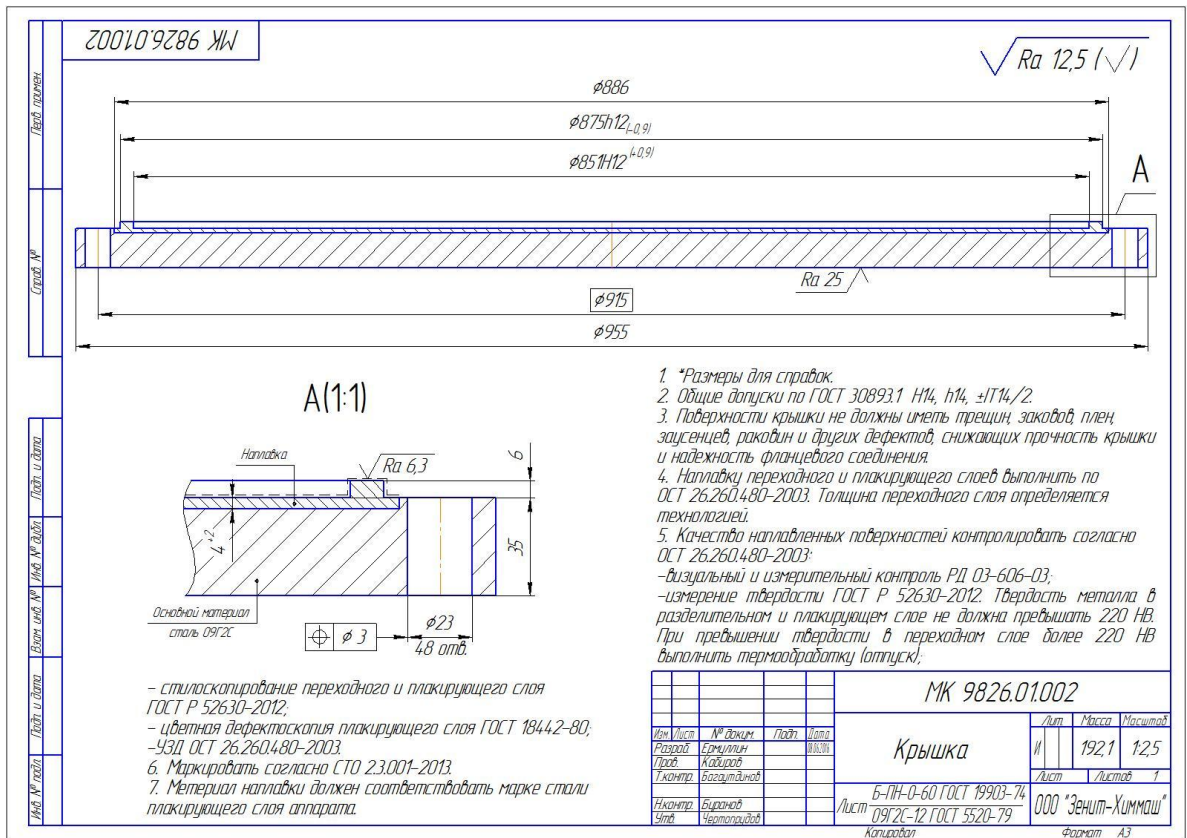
Чертёж крышки с наплавкой антикоррозионными материалами
